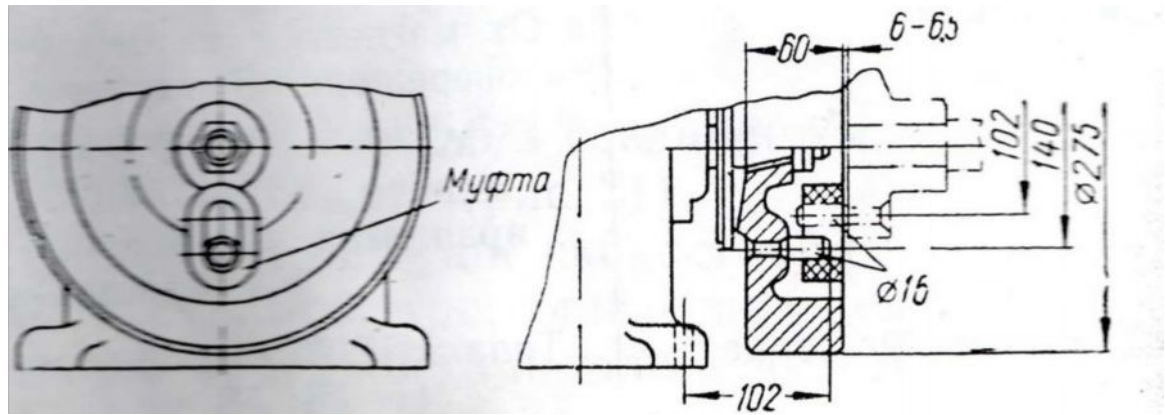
Соединение двигателя Л-6/3 с муфтой вала гребного винта.
